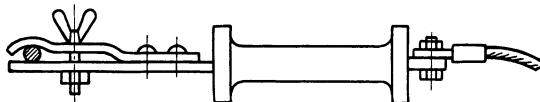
Schweißkolben für Warmschweißungen.
